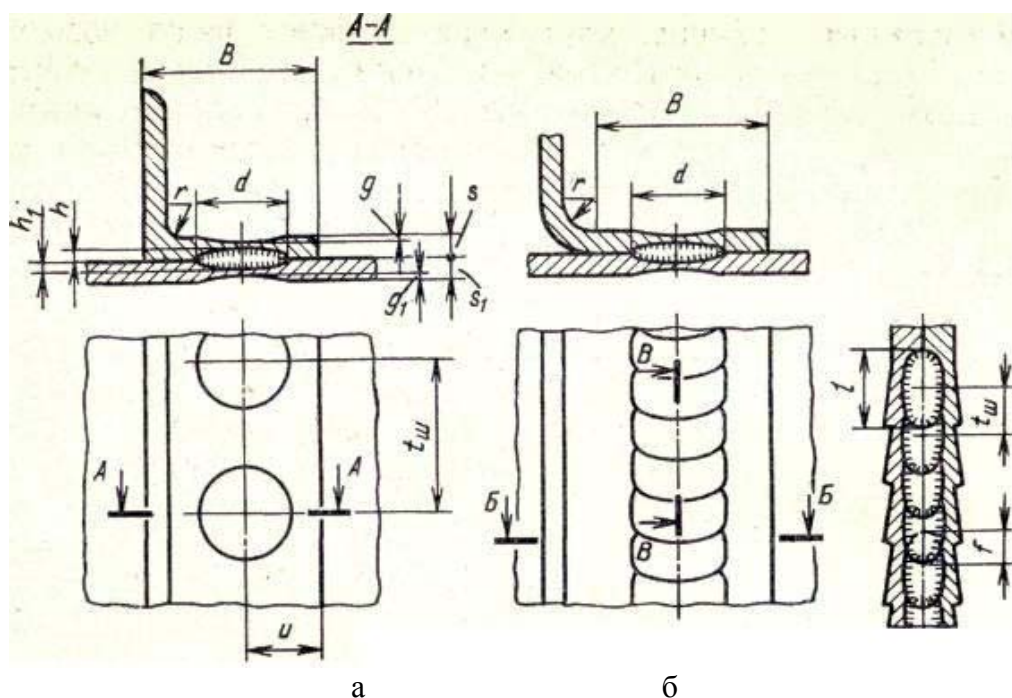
Конструктивные элементы соединений при сварке:
